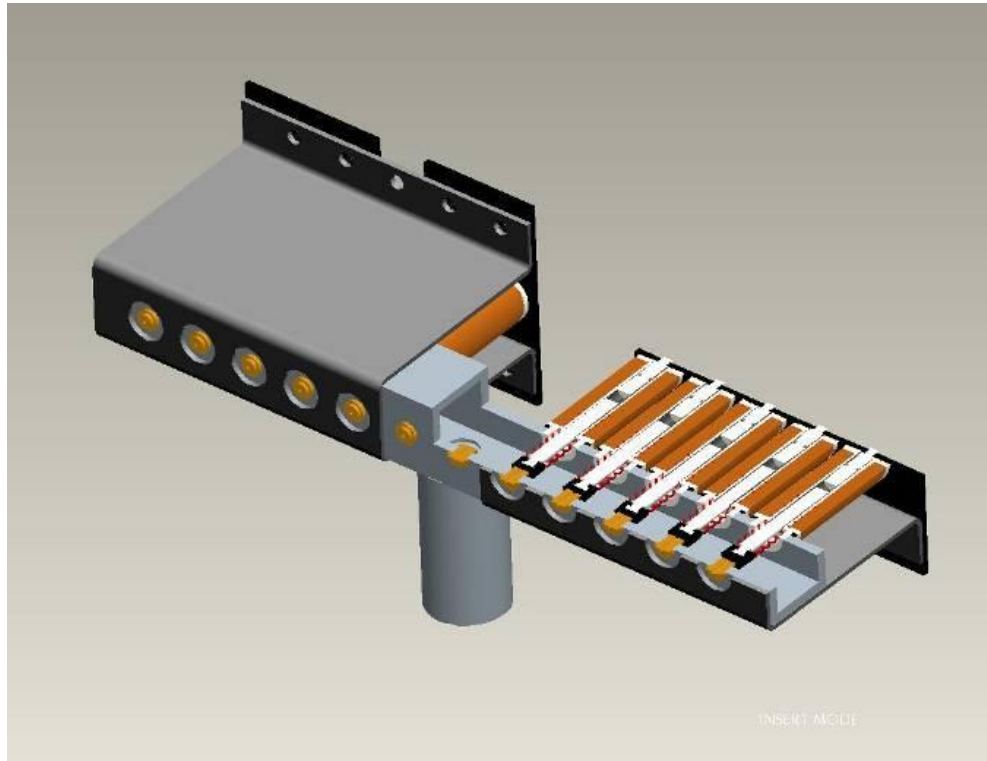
Vista em corte do conjunto de solenoides instalados no manifold
